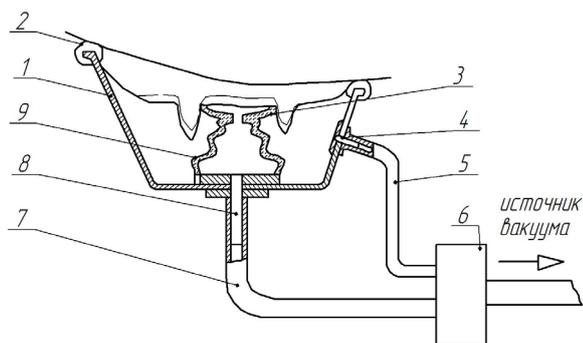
Схема устройства для массажа вымени животных однокамерного типа: 1 – кожух; 2 – уплотняющая прокладка; 3 – присосок; 4, 8 – патрубки; 5, 7 – шланги; 6 – пульсатор; 9 – пневмокамера
